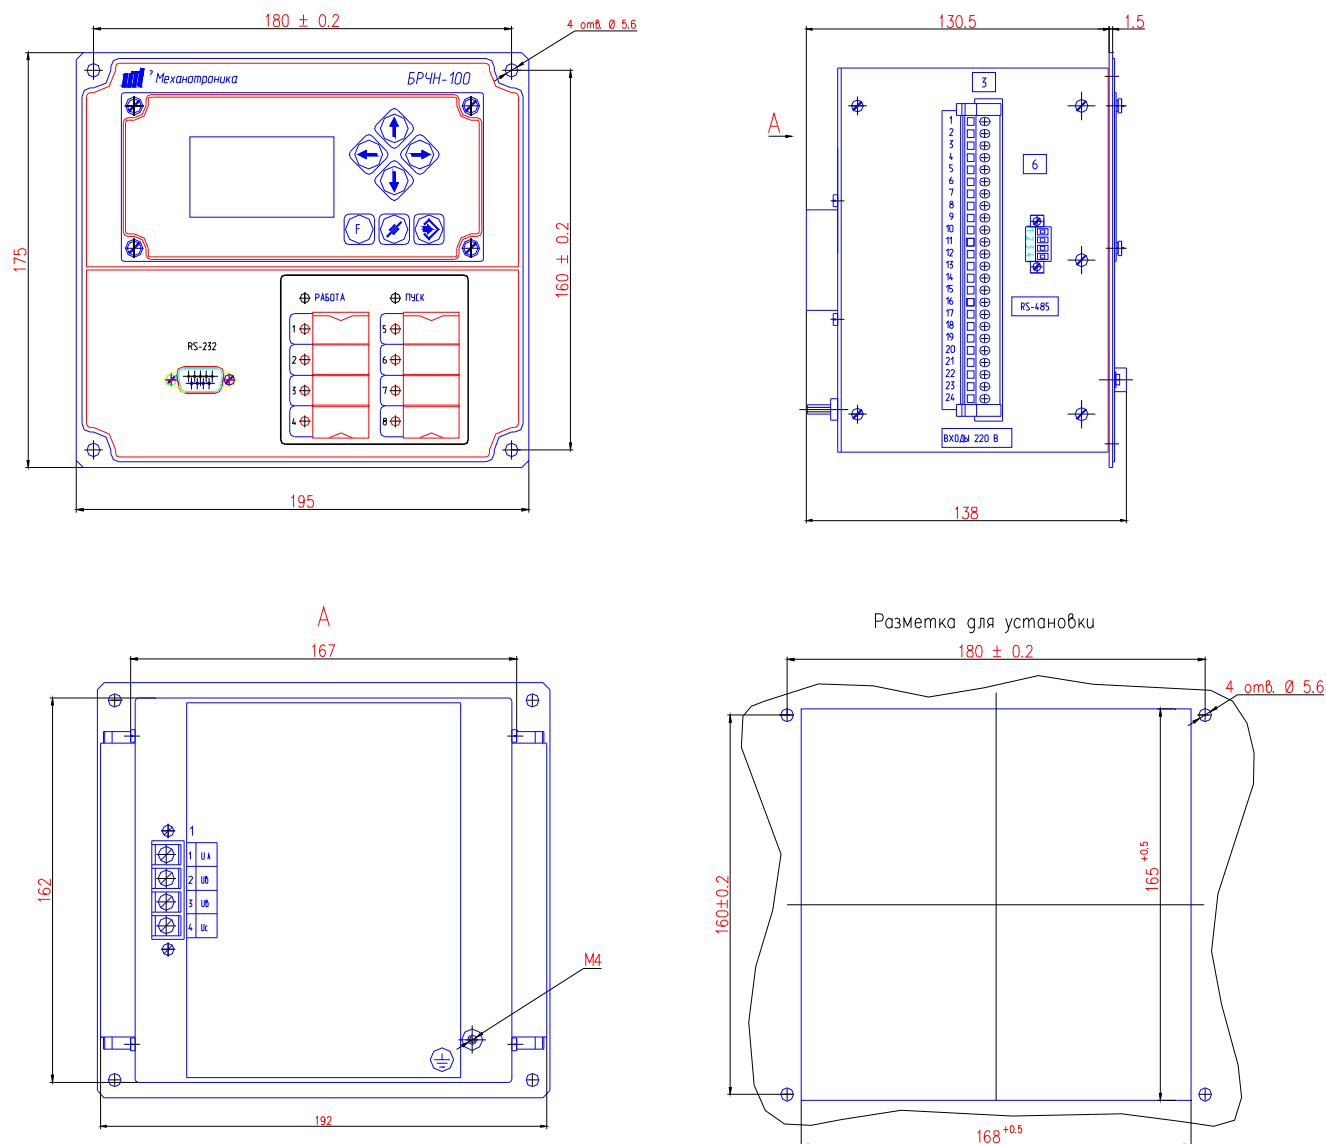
Габаритные, присоединительные и установочные размеры БРЧН-100
